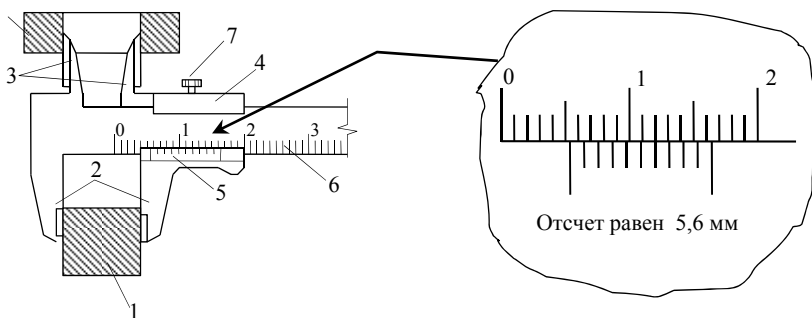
Схема измерения внешнего и внутреннего размеров с помощью штангенциркуля: 1 – измеряемые детали; 2, 3 – губки штангенциркуля; 4 – рамка; 5 – нониус с 10 делениями; 6 – штанга с делениями; 7 – зажимной винт
